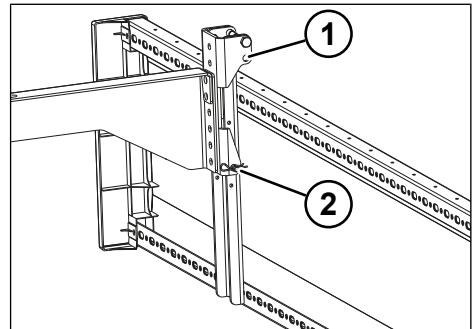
Dispositivo di protezione laterale abbassato (vista lato posteriore)
